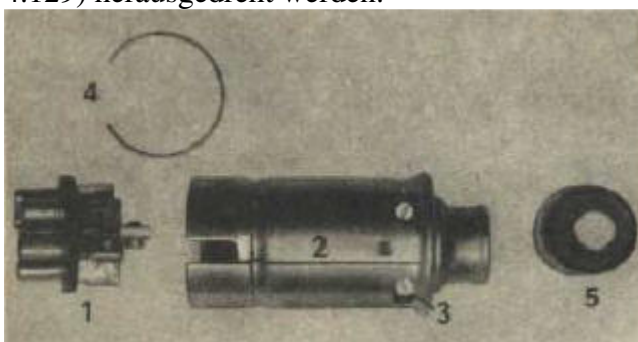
Anhängerstecker 1 Porzellangehäuse mit sieben federnden Steckanschlüssen; 2 Steckergehäuse; 3 Kabelschelle (innen liegend); 4 Sicherungsfeder; 5 Dichtkappe
